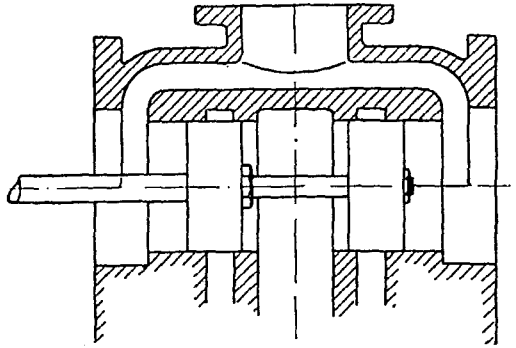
Цилиндрический двухкамерный золотник (Дёрфеля).
